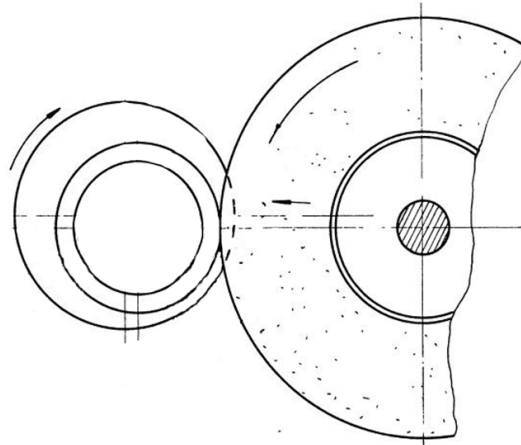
Схема шліфування зовнішніх поверхонь тіл обертання з базою від поверхні, що шліфується
